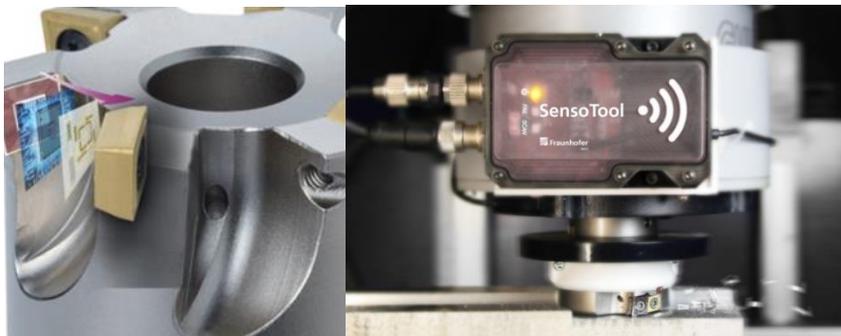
, Demonstrator »SensoTool«: Als »taktiles« Werkzeug registriert SensoTool Prozessgrößen dort, wo sie auftreten – direkt an den Wendeschneidplatten des Fräskopfes. | © Fraunhofer IWU |
